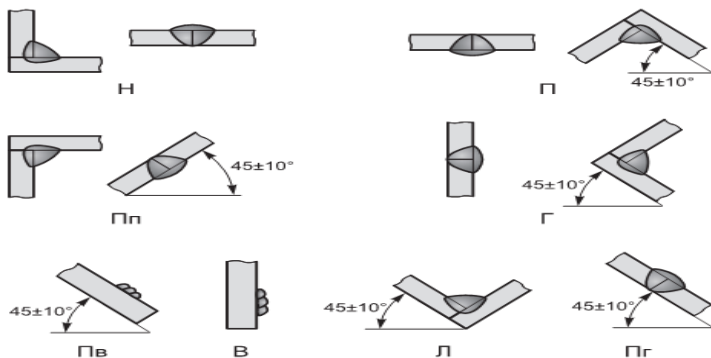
Обозначение сварных швов по их положению в пространстве:
